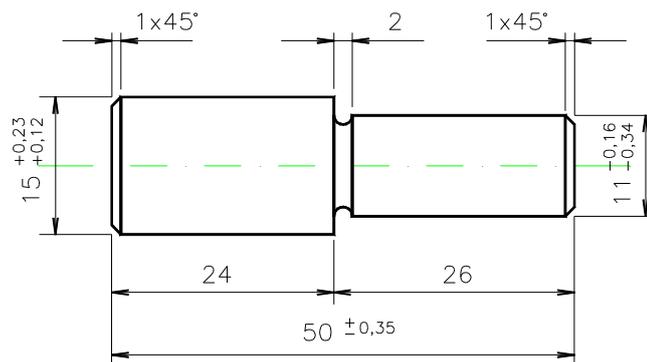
representação de dimensões nominais e seus afastamentos superior e inferior
